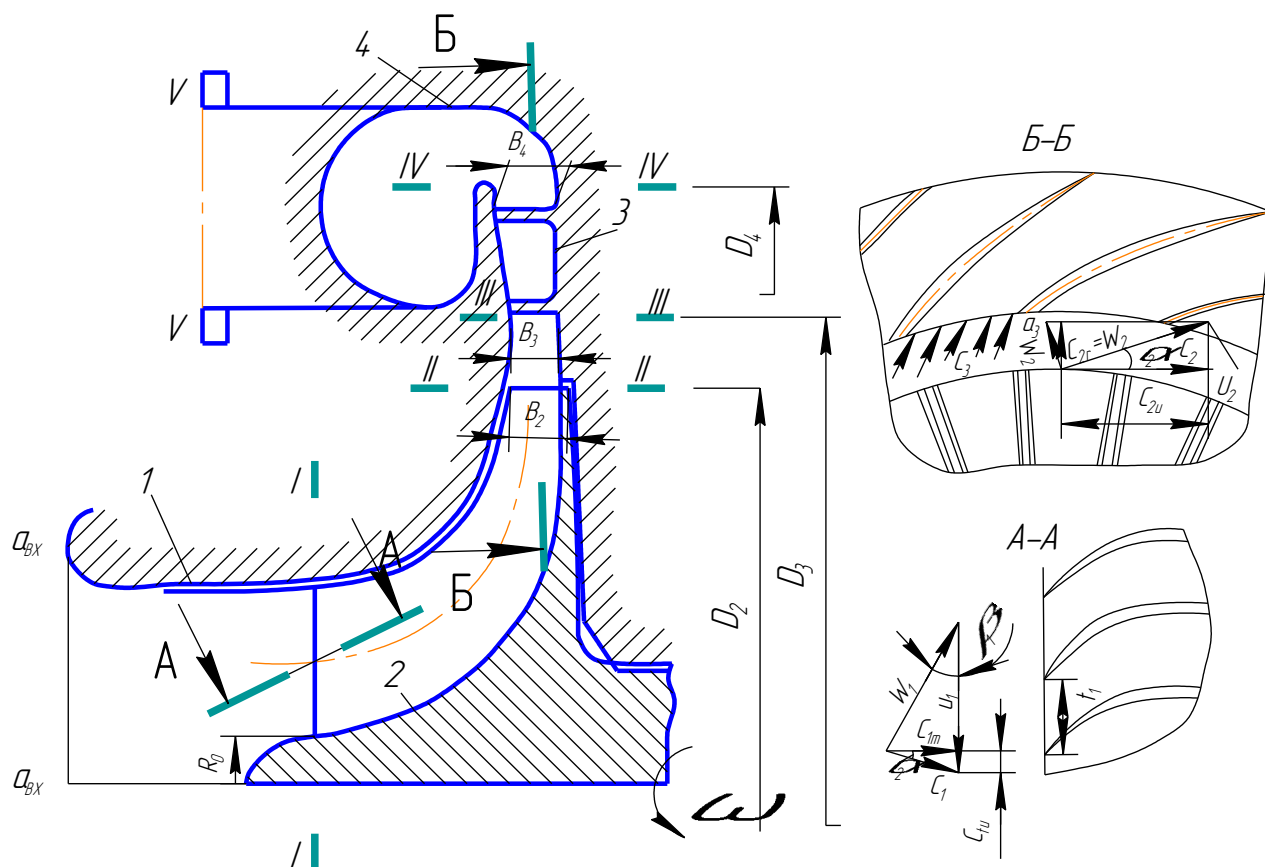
Схема проточной части центробежного компрессора с лопастым диффузором.
